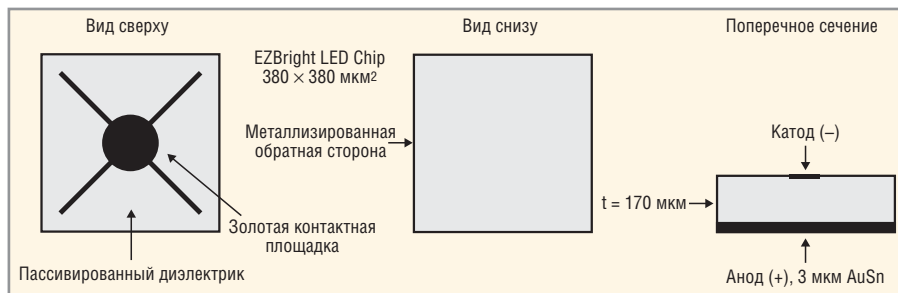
Габаритный чертёж чипов SxxxEZ400-Sxxx00-2
